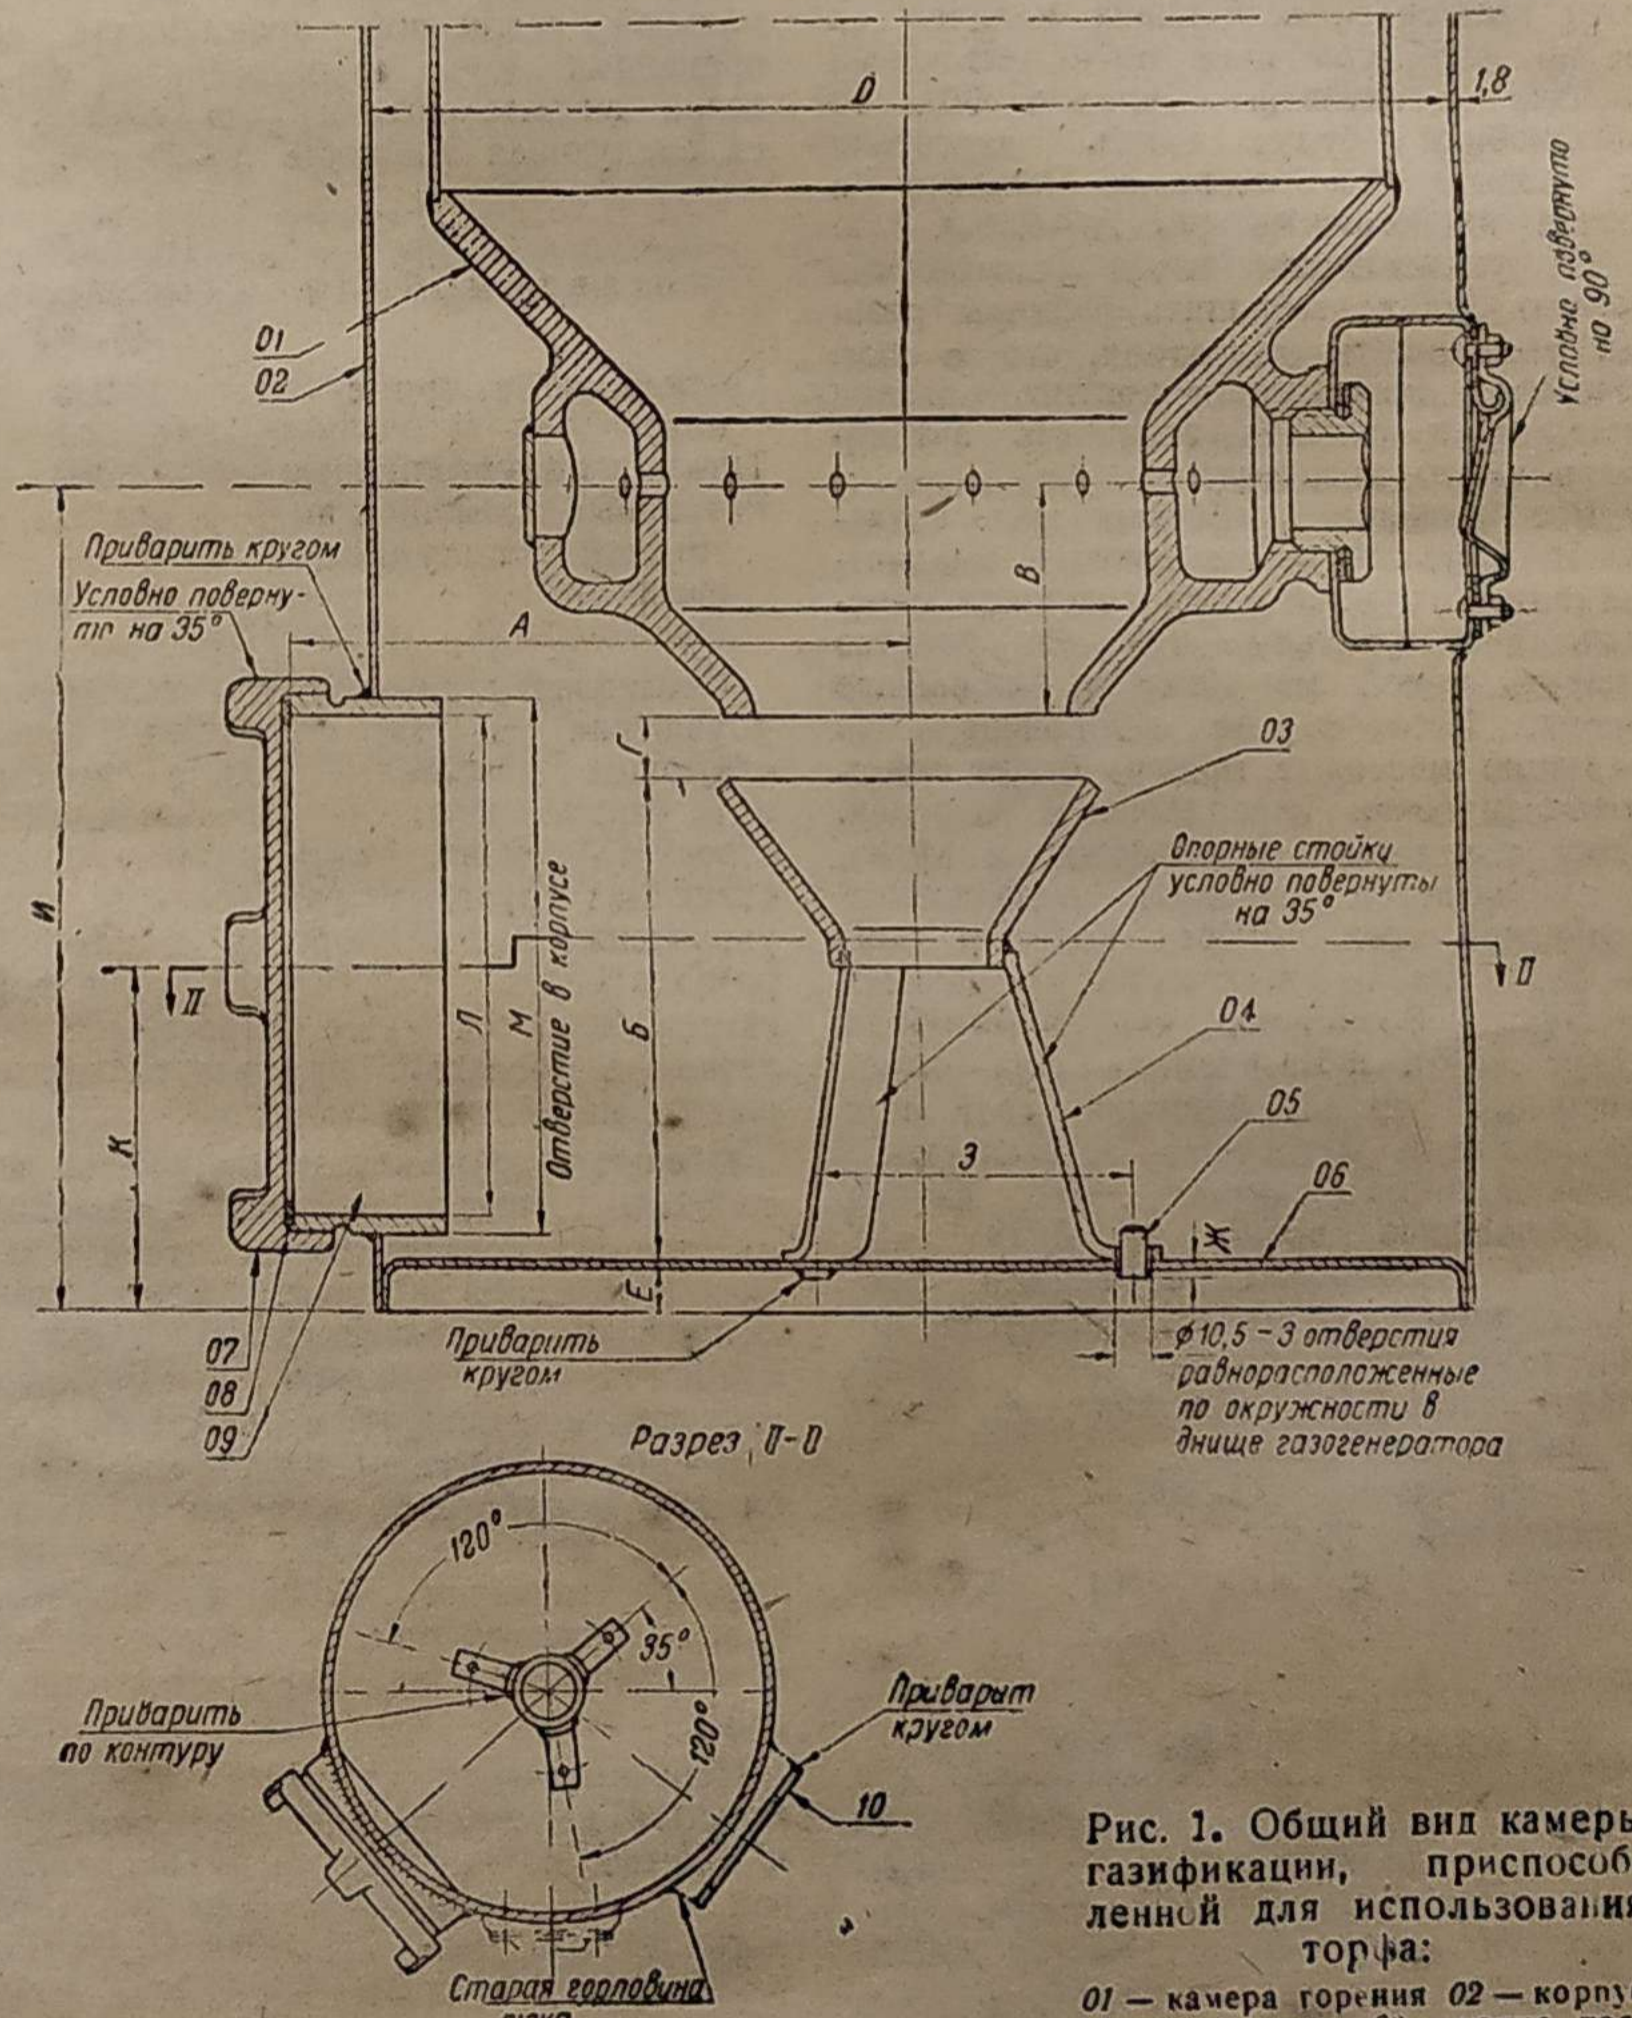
Общий вид камеры газификации, приспособленной для использования торфа:
